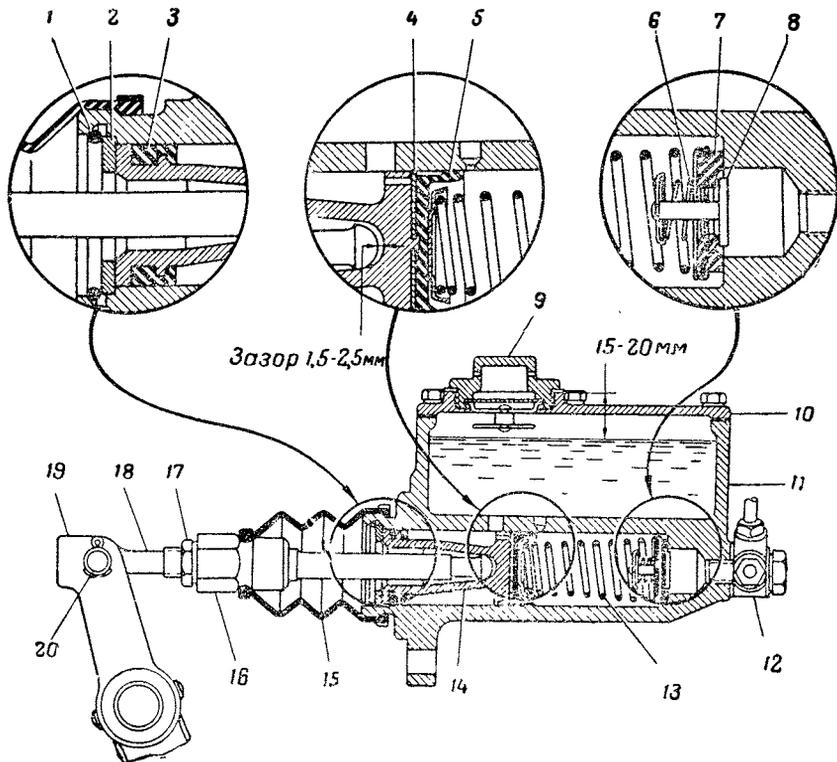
Регулировка зазора между толкателями и поршнем главного цилиндра:
